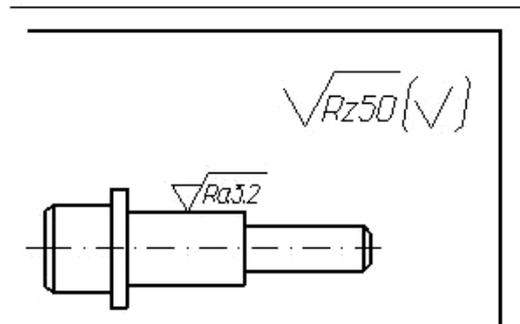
Указание шероховатости для большей части поверхностей изделия
